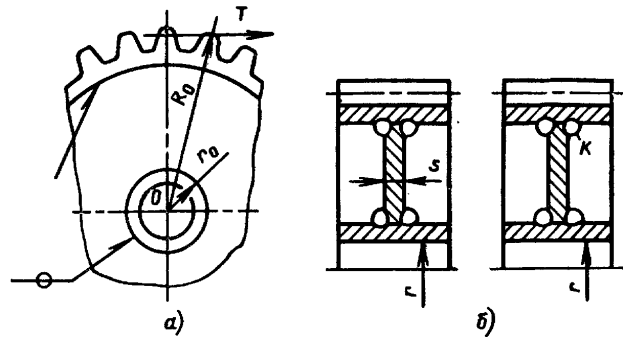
Схемы для расчета сварных соединений центра со ступицей:
